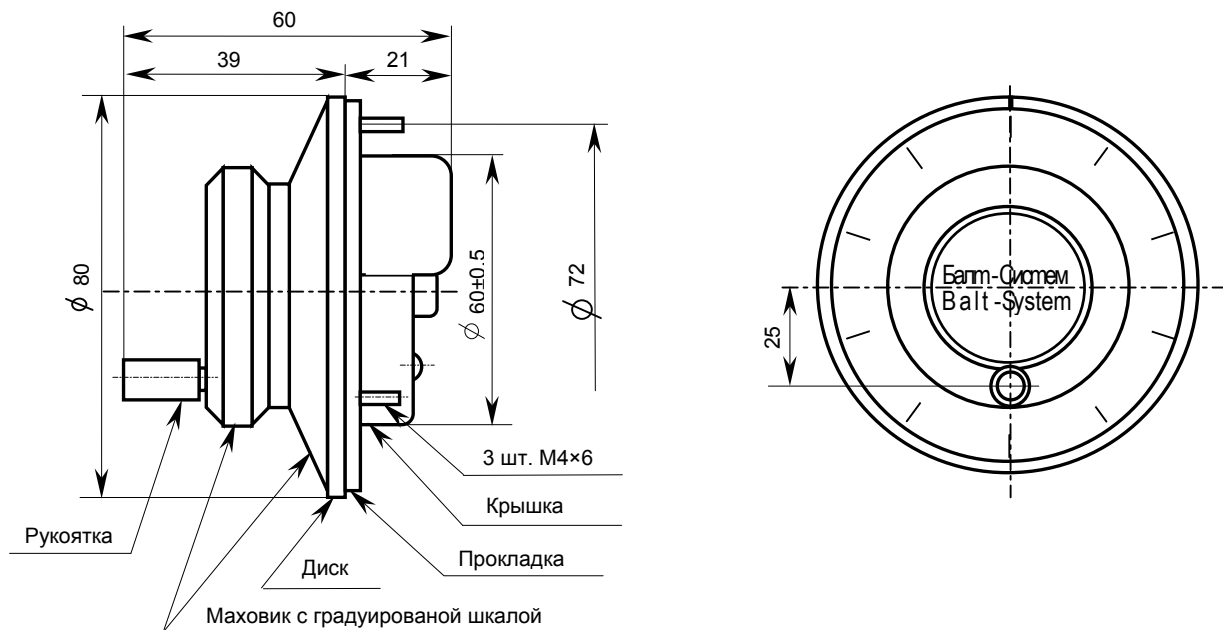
Габаритные размеры штурвала LGF-12-003B-100
